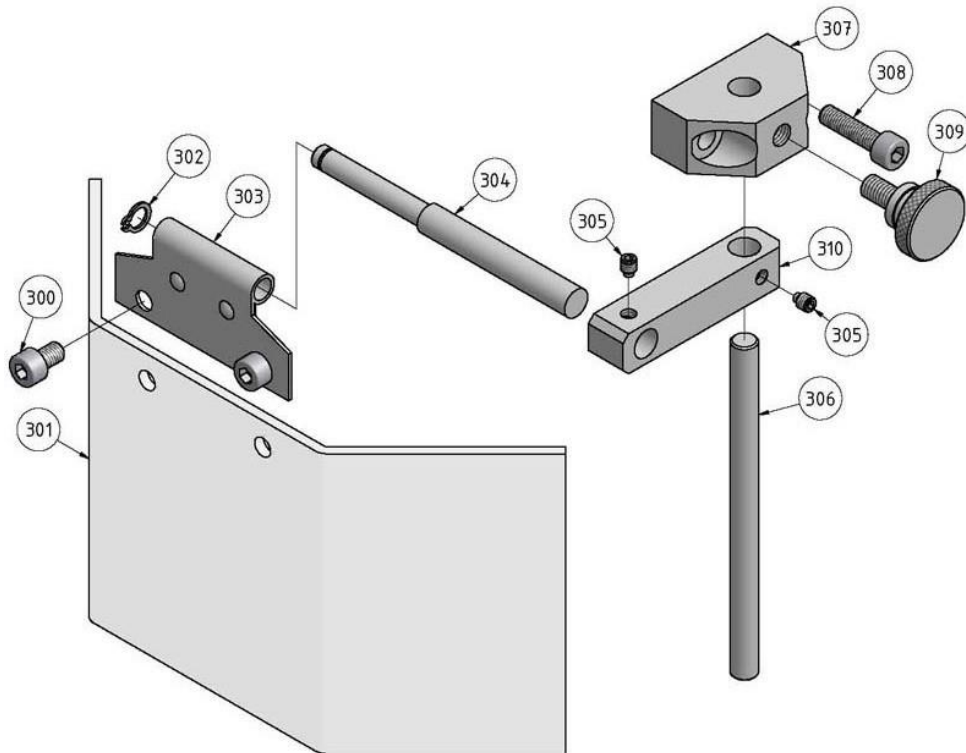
Fräsfutterschutz - Milling chuck protection
